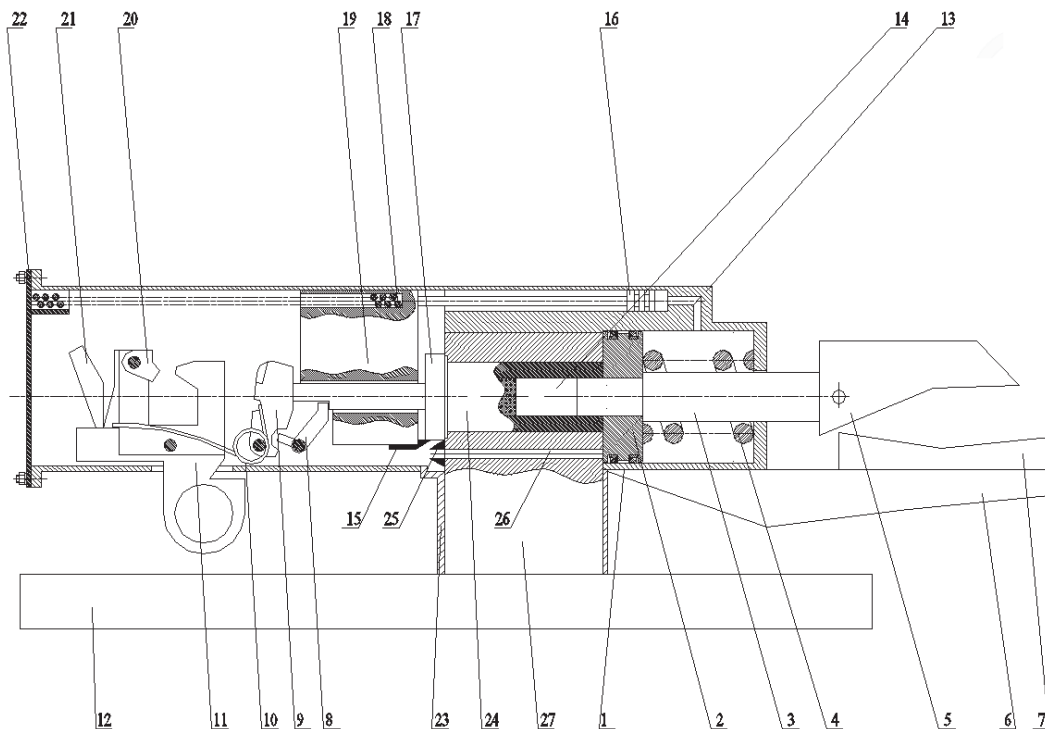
Різучий вузол для різання дротів при проведенні заходів з розмінування вибухових пристроїв: 1 – корпус; 2 – поршень з ущільненнями; 3 – шток; 4 – зворотна пружина; 5 – рухомий ніж; 6 – скоба; 7 – нерухомий ніж; 8 – шептало автоспуску; 9 – курок; 10 – пружина; 11 – спусковий гачок; 12 – основа пристрою вузла різання; 13 – газовідводна трубка; 14 – рухомий шток набойю; 15 – собачка; 16 – поршень штоку затворної рами; 17 – затвор з ударником; 18 – пружина; 19 – затворна рама; 20 – засувка сповільнювача курка; 21 – запобіжник; 22 – задня кришка; 23 – опорно-захисні пластини; 24 – гільза набойю з капсулем та порохом; 25 – зубці храпового колеса; 26 – вісь барабану; 27 – барабан.
